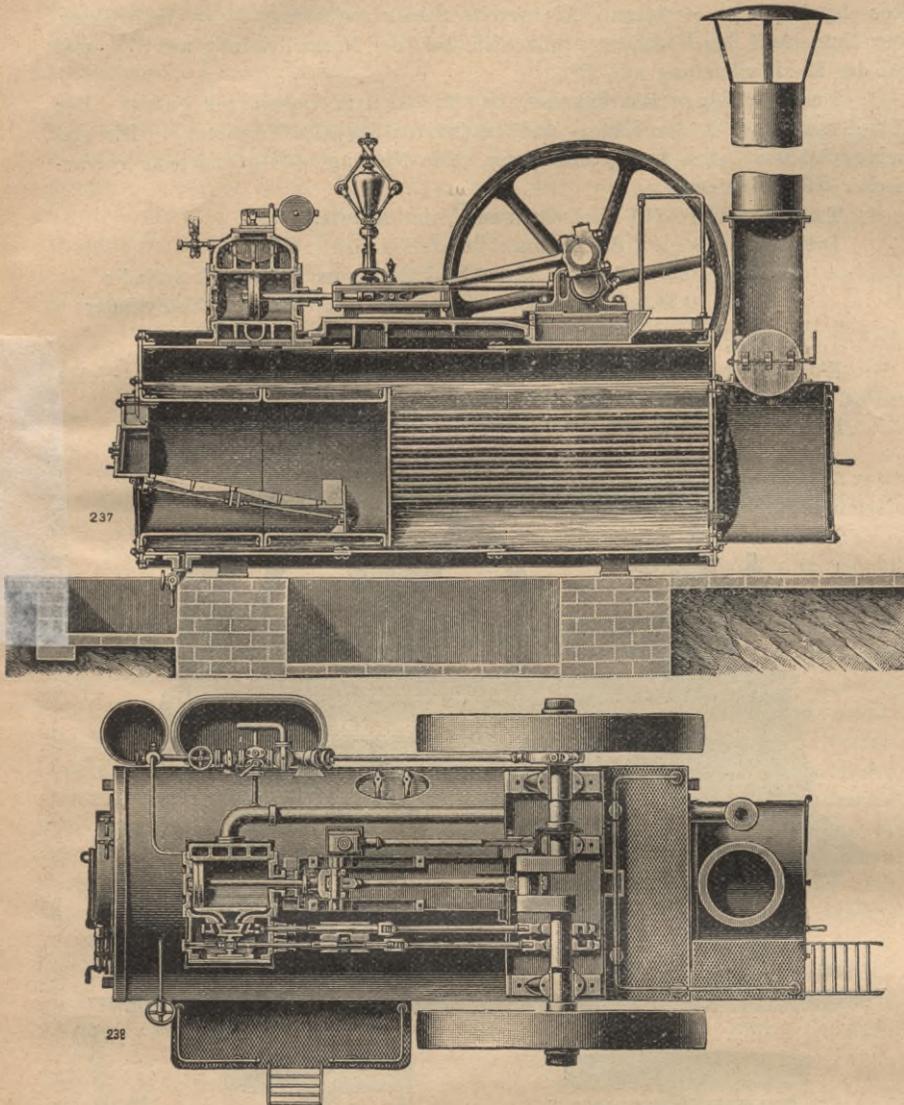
Längsansicht und Grundriß einer Wolfschen Hochdruck-Lokomobile auf Tragfüßen mit selbstthätiger Riderscher Expansions-Steuerung.
